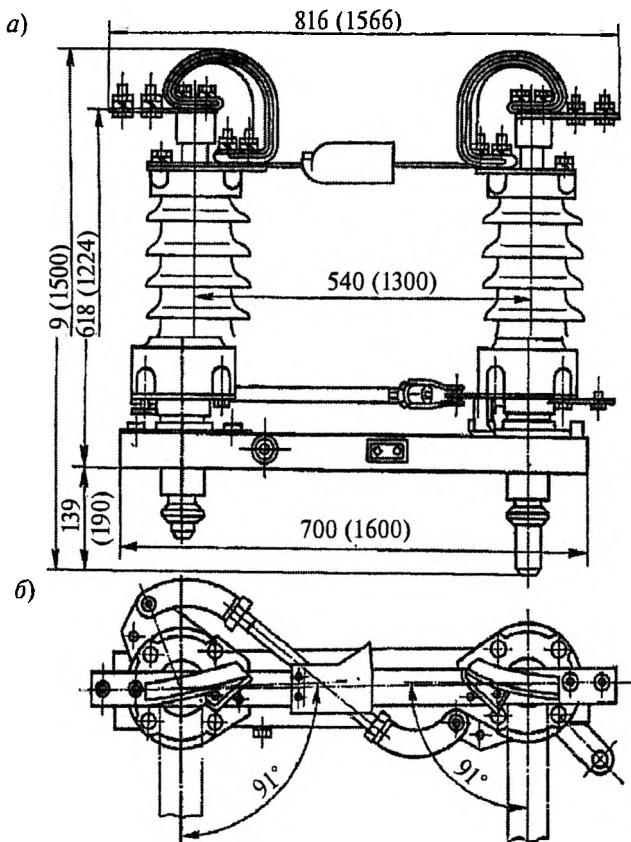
Разъединитель наружной установки РЛНД-35 (размеры без скобок) и РЛНД-110 (размеры в скобках):
